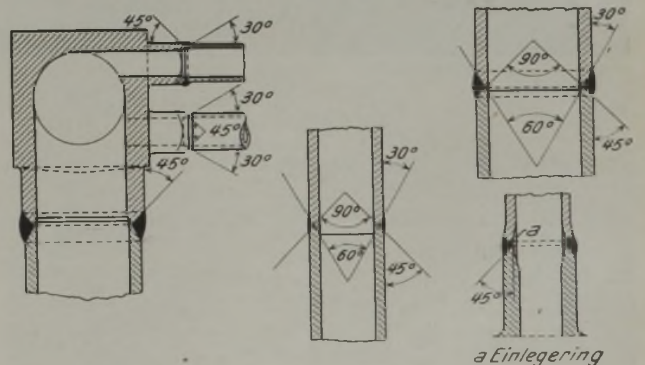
Schweißverbindungen an den Hochdruckkesseln.
